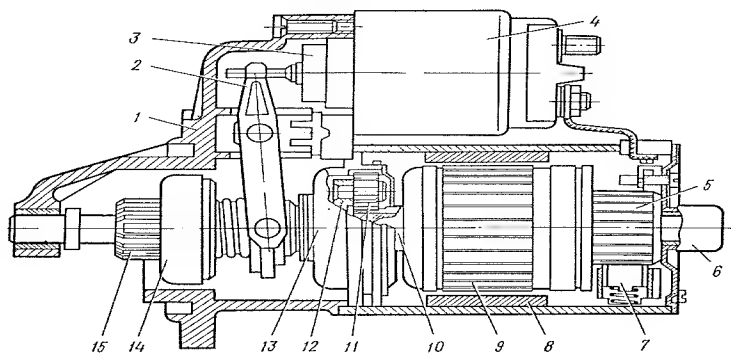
Стартер с планетарным редуктором и возбуждением от постоянных магнитов [8]:
